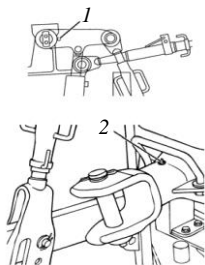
Смазка втулок поворотного вала задней навески и буксирного устройства:
